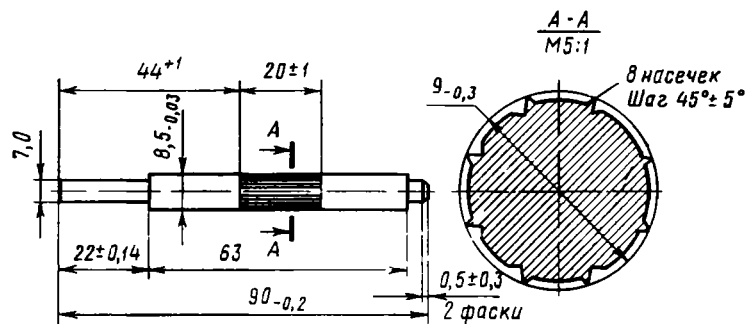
Вал для крепления на нем сердечника прессовой пластмассы
